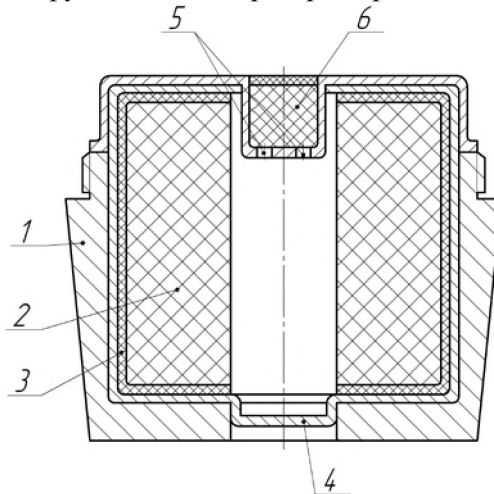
Газогенератор: 1 – корпус; 2 – топливный заряд; 3 – бронировка; 4 – заглушка; 5 – отверстия; 6 – воспламенительное устройство
